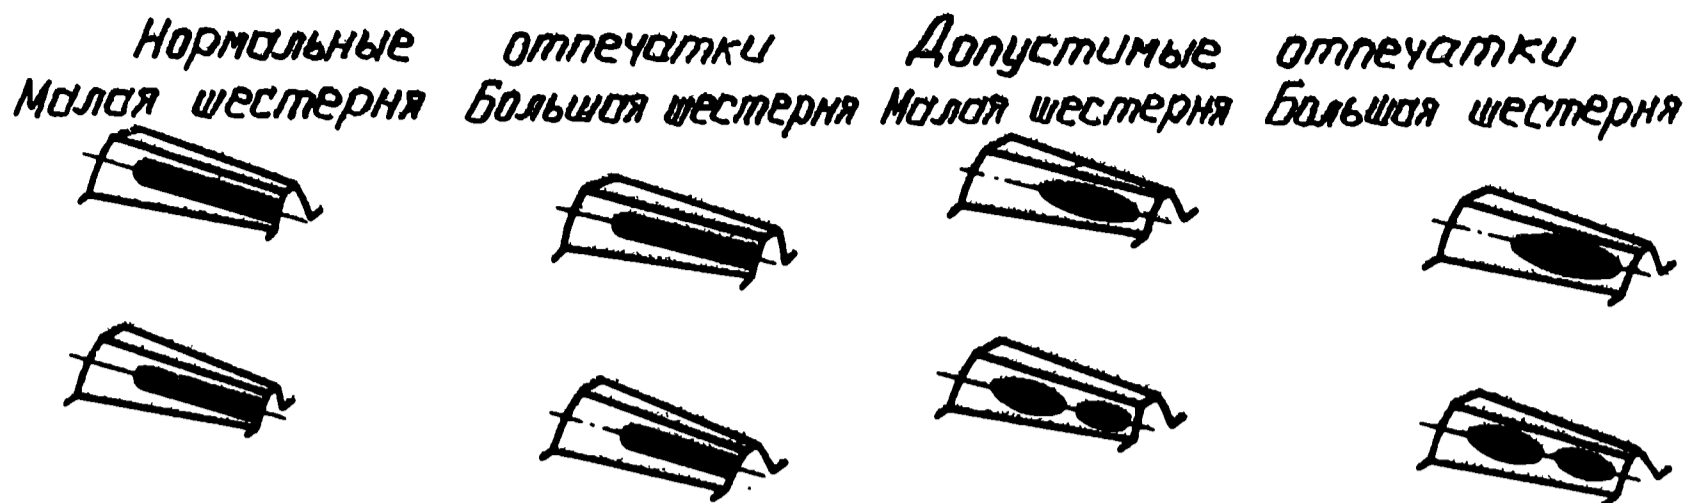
Схема расположения отпечатков на зубьях шестерни главной конической передачи
